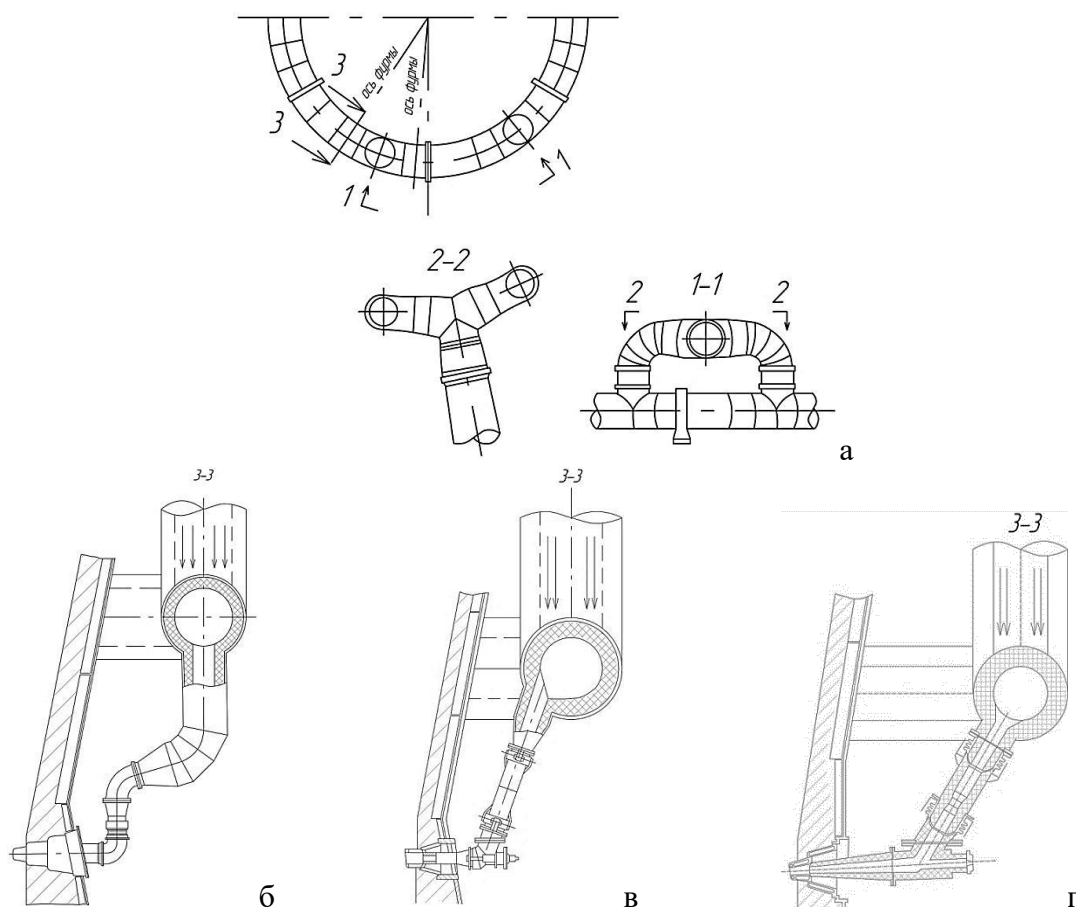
Односторонний подвод (сверху) горячего дутья к кольцевому воздухопроводу с двумя патрубками: а – прямой подвод горячего дутья; б – фурменные приборы типовой конструкции; в – конструкция фурменного прибора «Гипромега»;
